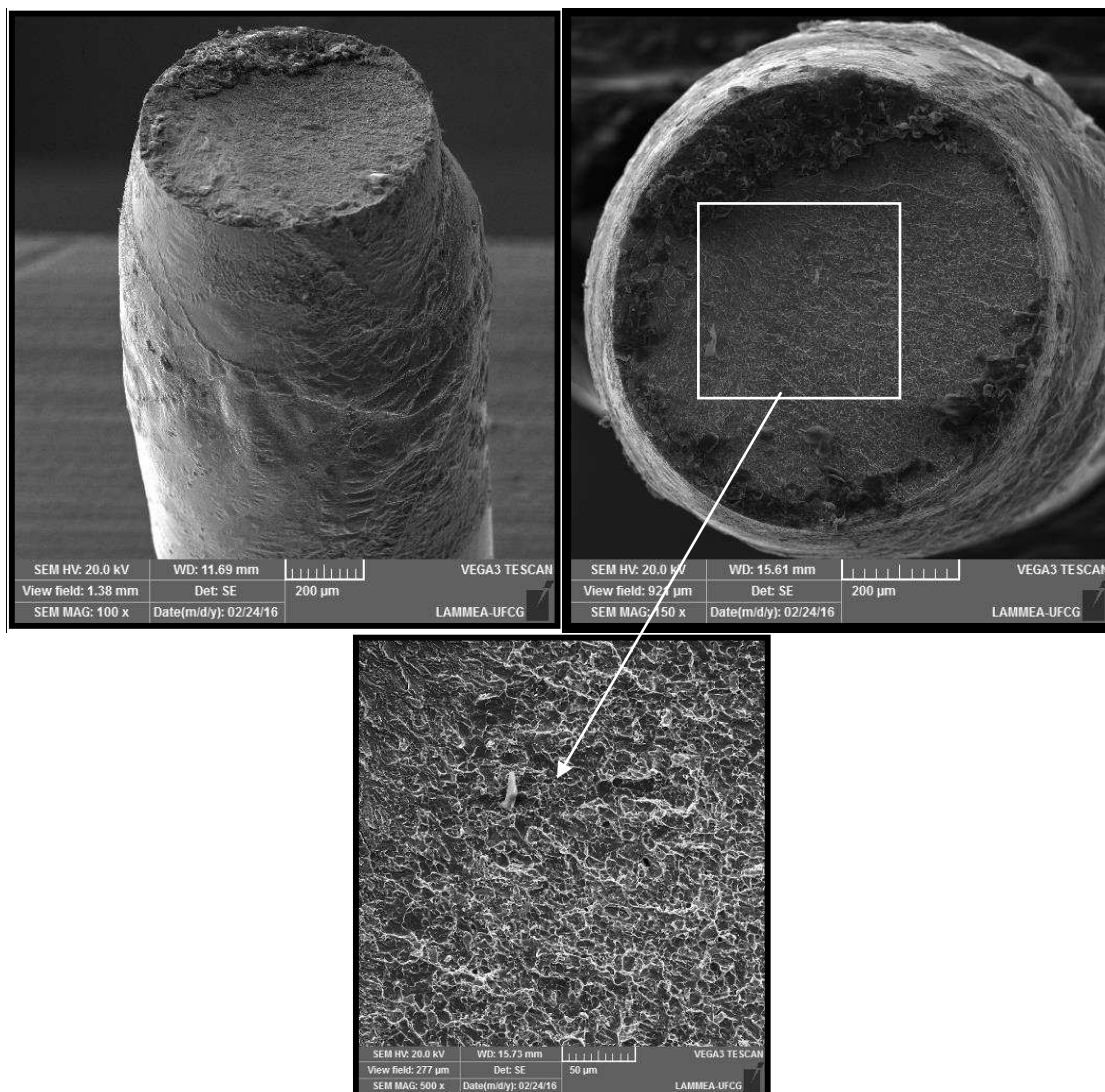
Superfície de fratura do fio superelástico soldado na configuração 7ms/70% e testado a 40°C.
